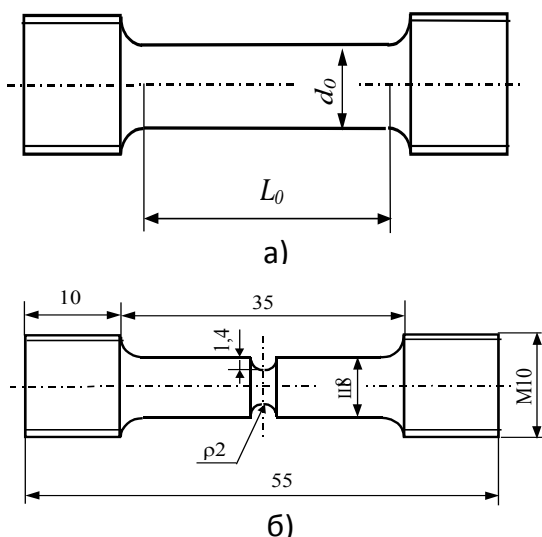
Схема: а) гладкого цилиндрического образца; б) цилиндрического образца с кольцевым надрезом
